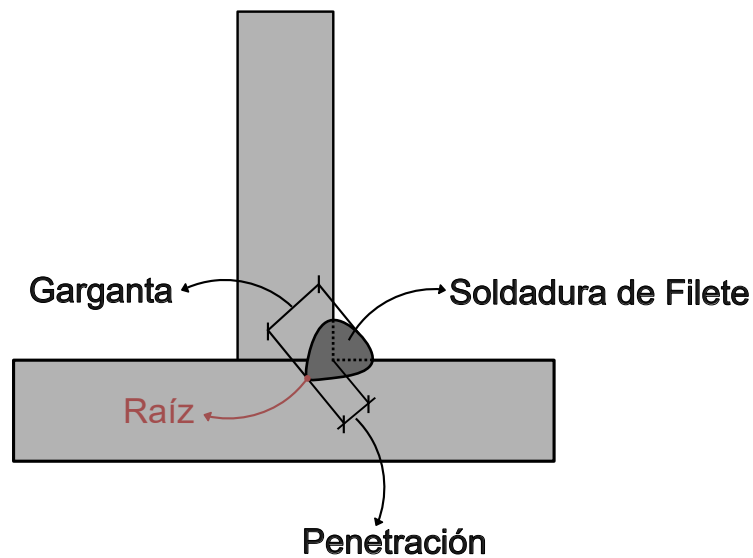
Partes de la soldadura de filete [17][22].
